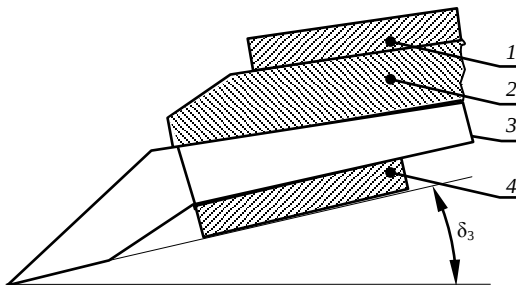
Схема установки зуба ковша экскаватора-дреноукладчика
